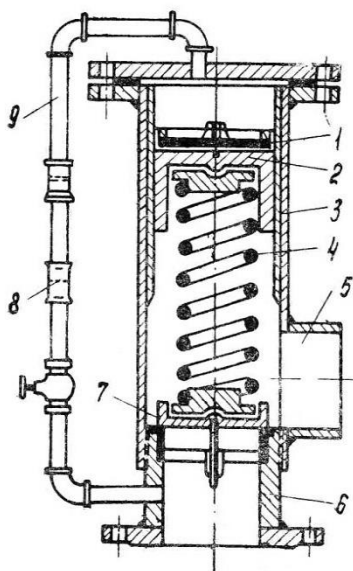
Предохранительные пружинные устройства: 1 - самоуплотняющаяся кожаная манжета, 2 - бронзовый поршень, 3 - корпус, 4 - пружина, 5 - сбросной патрубок, 6 - присоединительный патрубок, 7 - бронзовый клапан, 8 - диафрагма, 9 - трубка.
